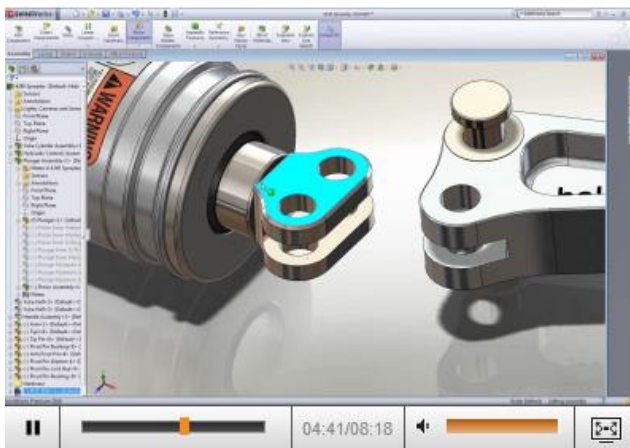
Conjunto montado no SOLIDWORKS – 3D CAD
